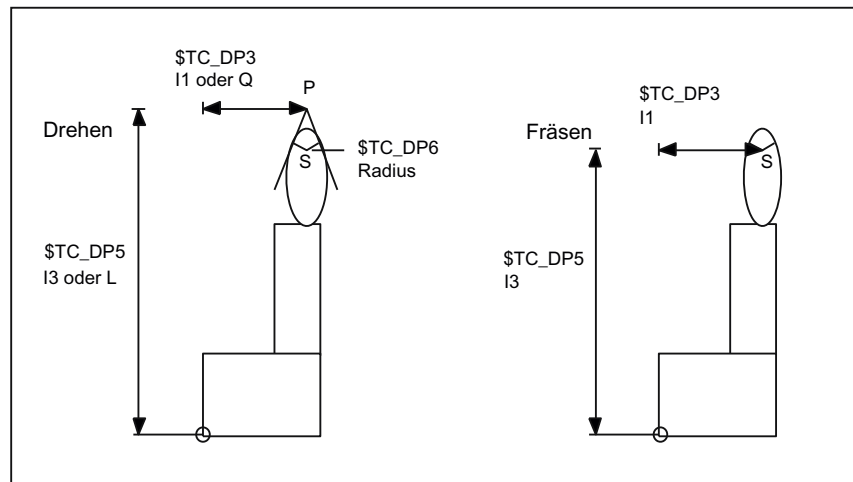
Dreh- und Fräs-Werkzeuge - Zusammenhang Schnittpunkte und Radiuskorrektur
